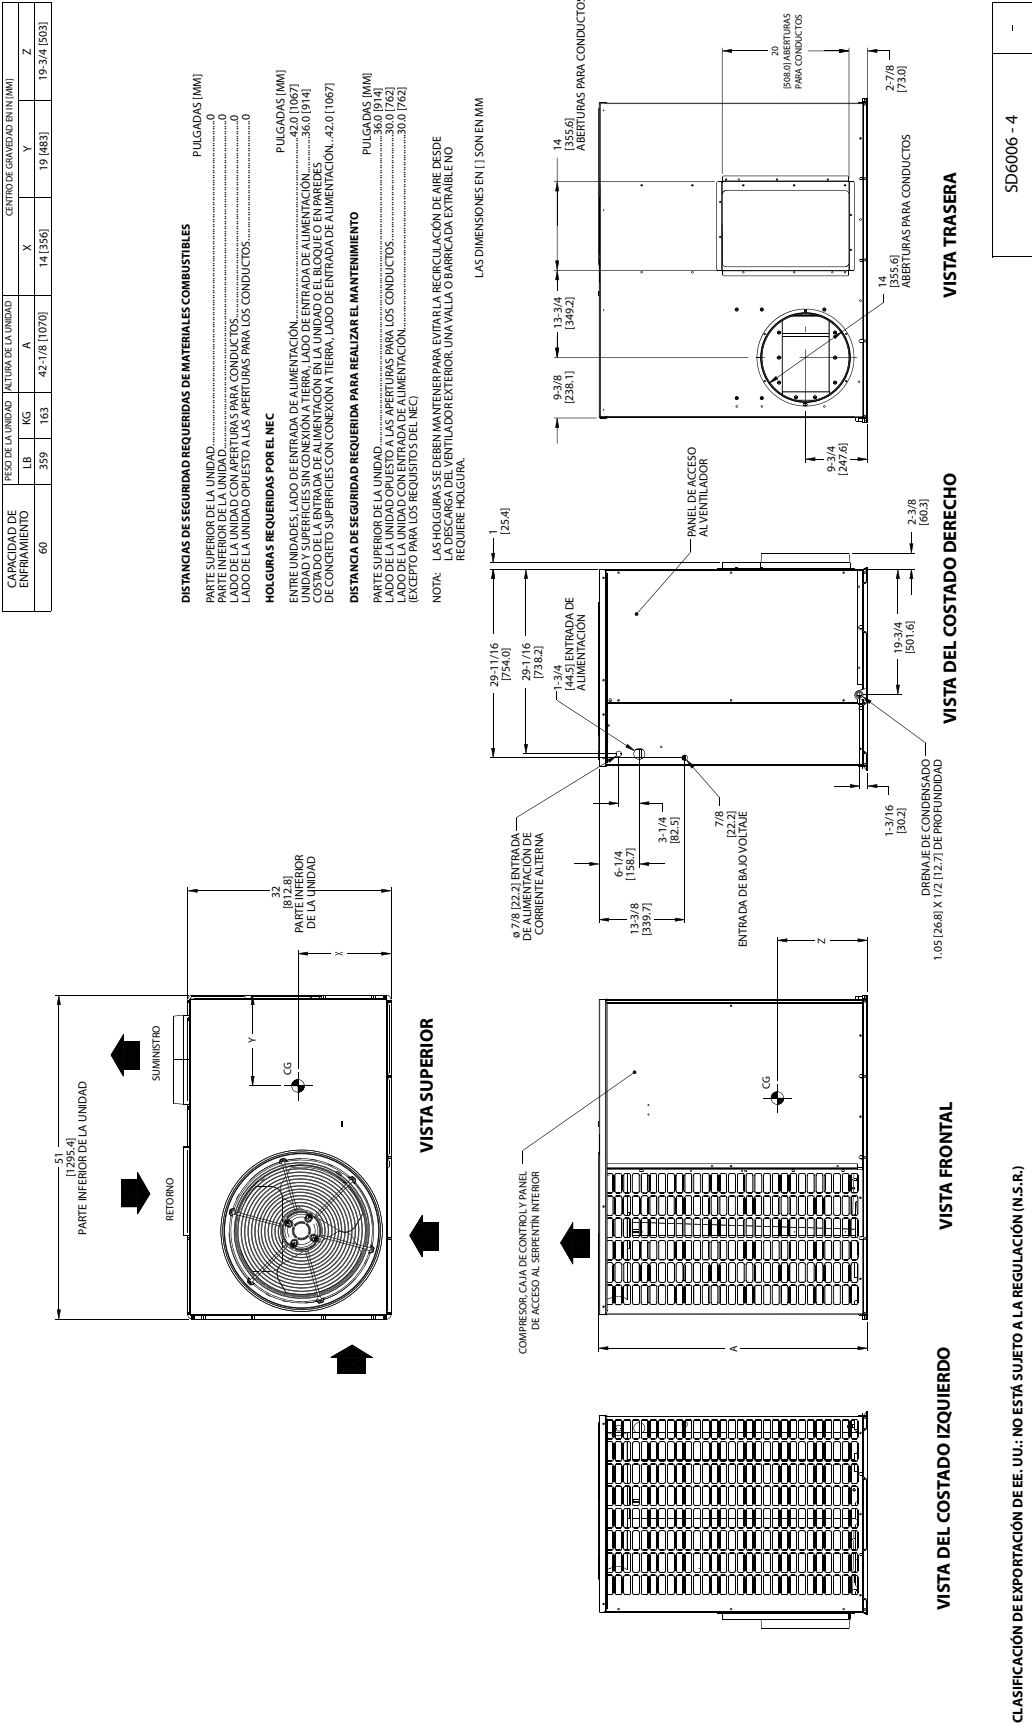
Dimensiones de la base de la unidad 50NPB 060
